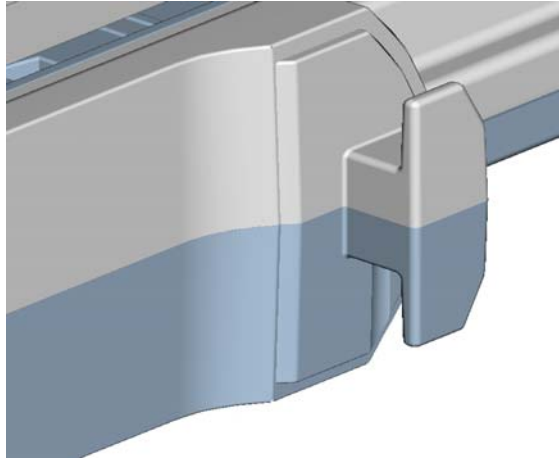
Dělicí rovina konstruovaná v modulu Mold Cavity Pro/E u výlisku číslo N060006
